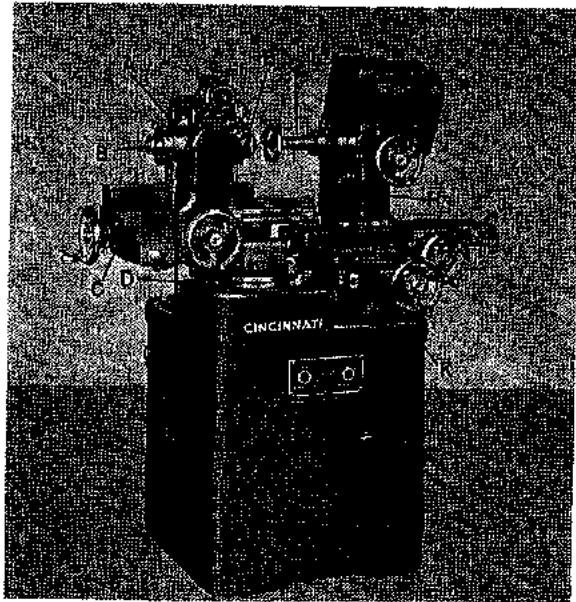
Rectificadora universal de fresas y herramientas (Cincinnati Milling Machine Co.)
